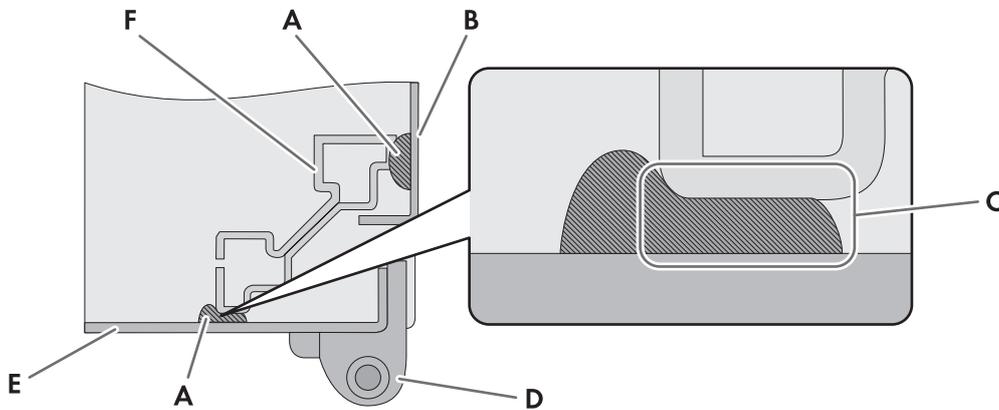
Schnittzeichnung der Draufsicht einer Türdichtungen (Beispiel)
